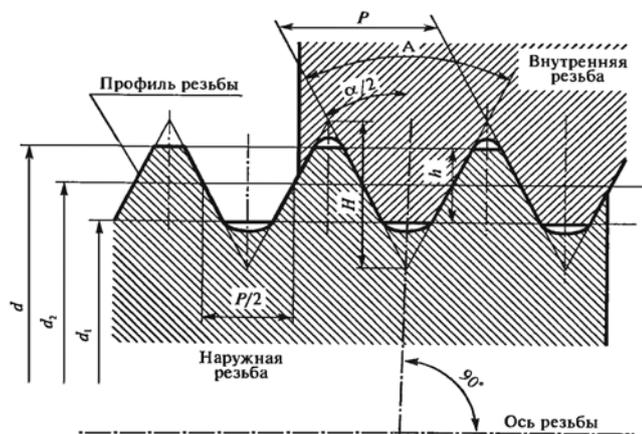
Номинальный профиль цилиндрической метрической резьбы.  $d_2$  – средний диаметр
